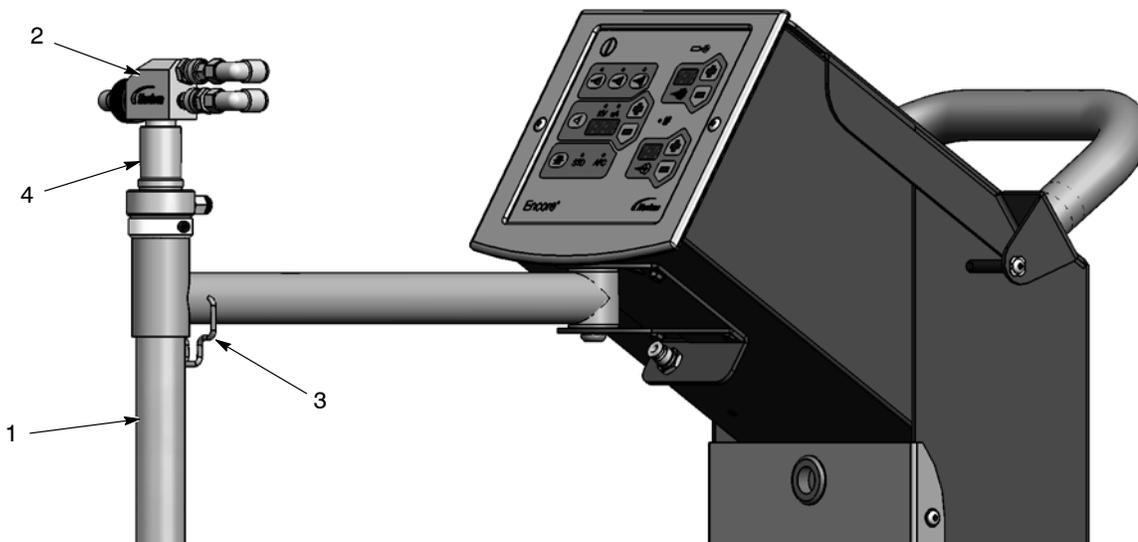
Монтаж всасывающей трубки и насоса распылителя Encore LT
